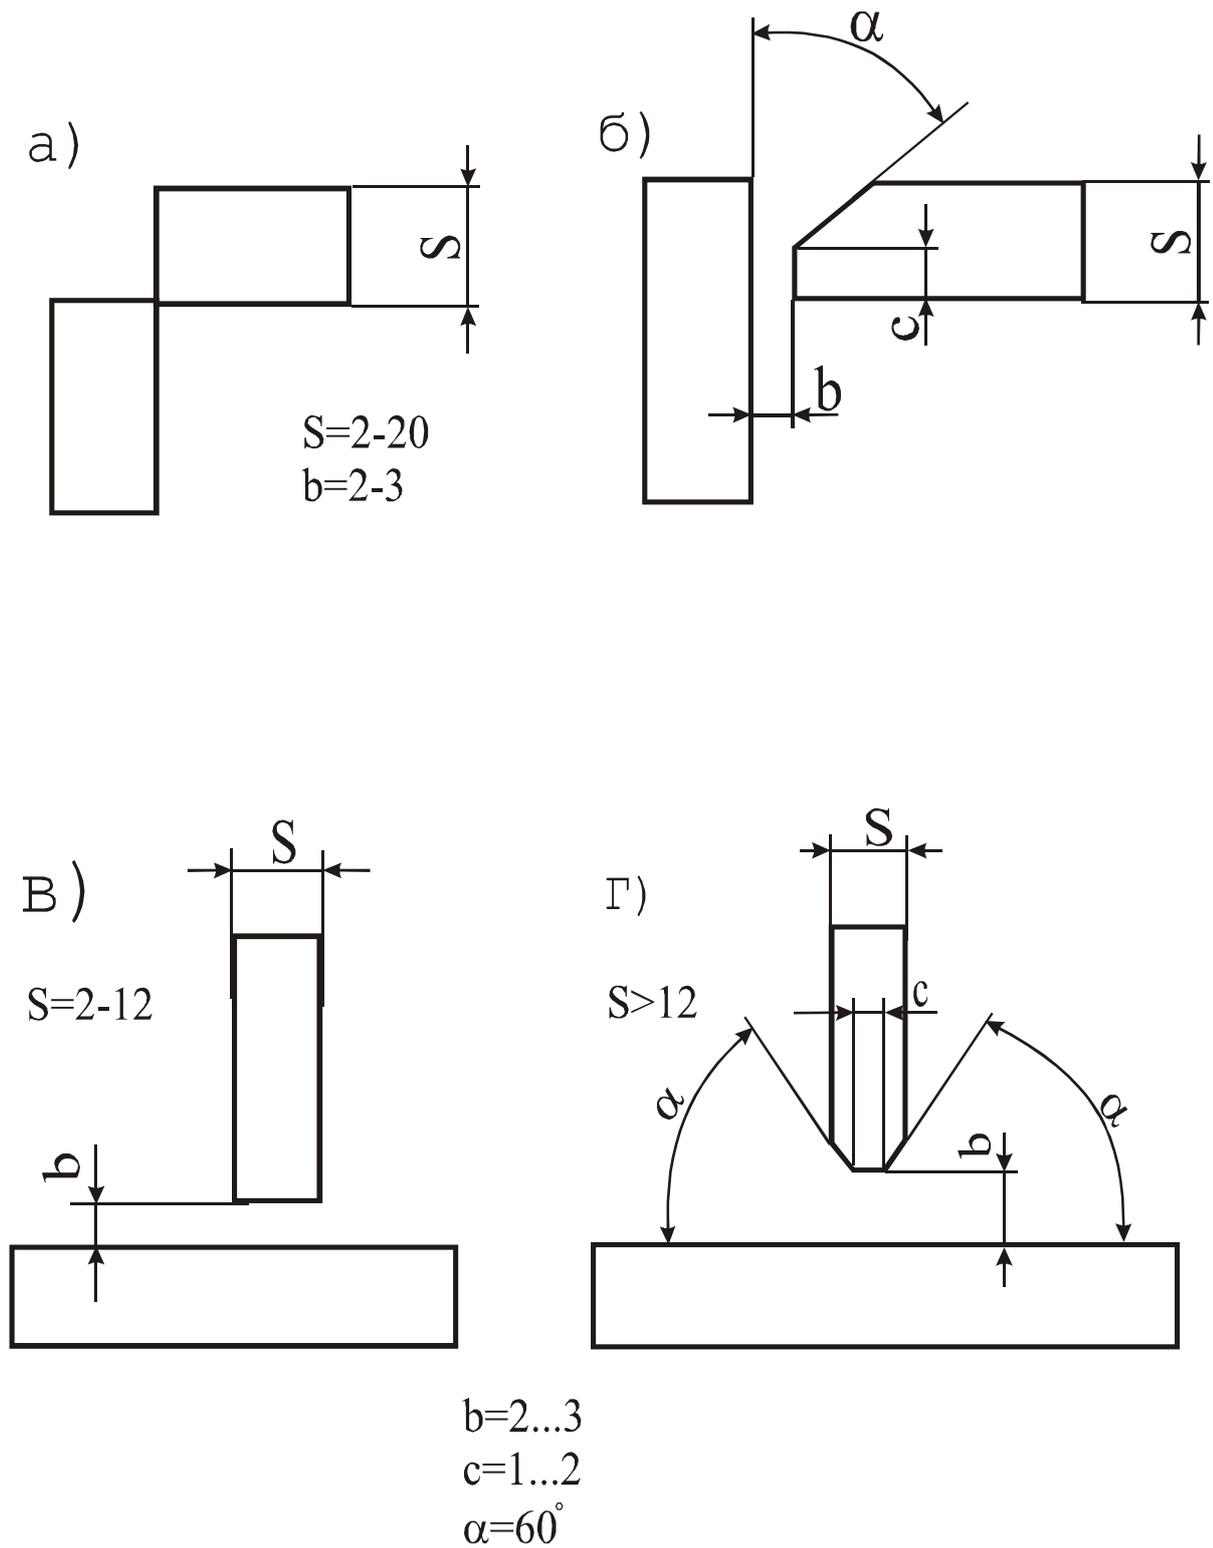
Виды угловых и тавровых соединений: а) угловое без разделки кромок; б) угловое с разделкой кромок; в) тавровое без разделки кромок; г) тавровое с разделкой кромок.
